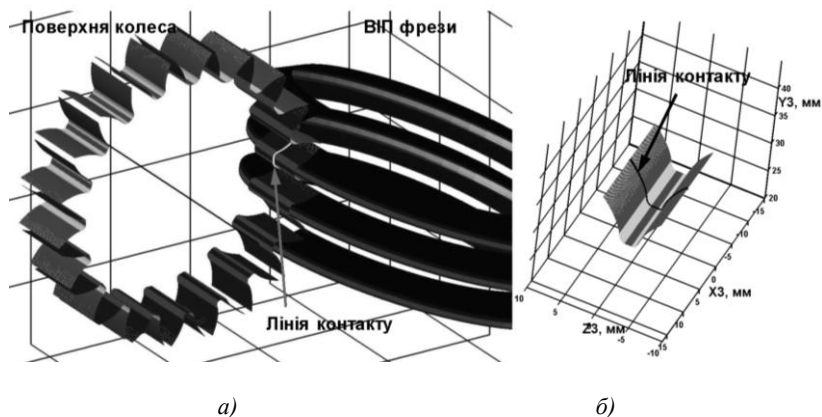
Розрахунок поверхні спряженого колеса з фрезою:
